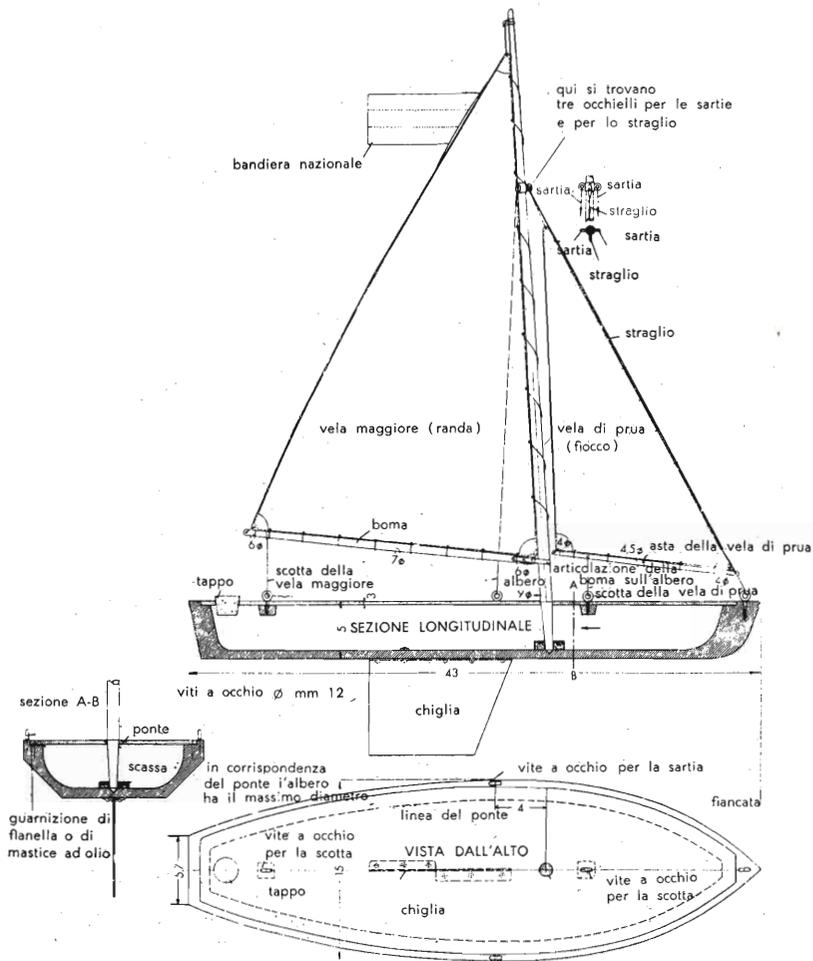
Modello ricavato dal pieno in sezione longitudinale e trasversale e visto dall'alto.
